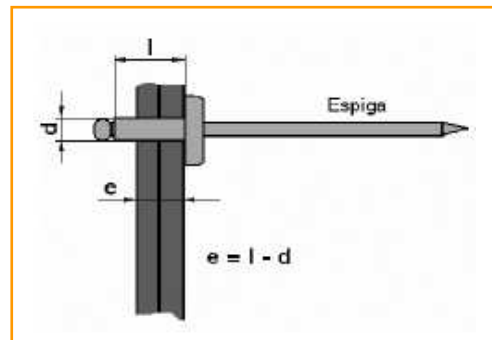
Dimensiones de un remache y espesor máximo de las chapas a unir.
